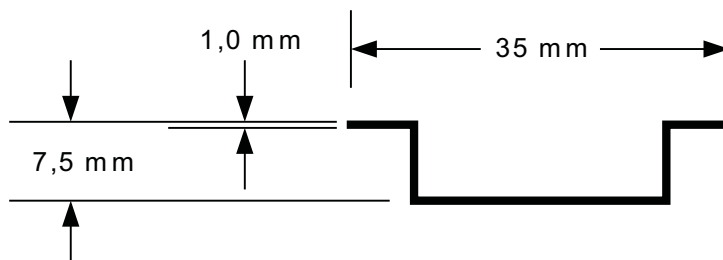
Dimensiones para el montaje en un perfil soporte
